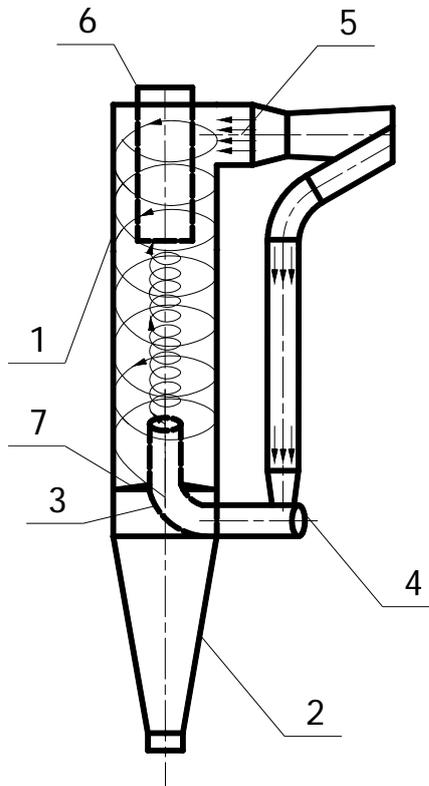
Вихревой пылеуловитель со встречными закрученными потоками: 1 – корпус; 2 – пылесборник; 3 – осевой патрубок; 4 - завихритель; 5 – тангенциальный патрубок; 6 - вывод очищенного газа.
